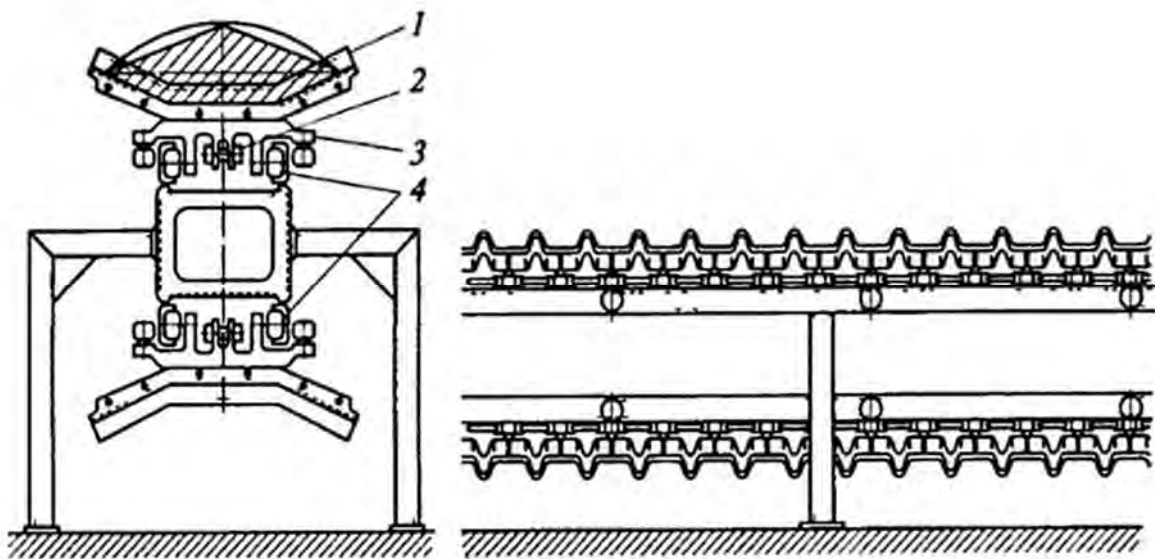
Пространственный пластинчатый конвейер: 1 – настил; 2 – цепь с соединительным звеном; 3 – опорное устройство; 4 – каток
